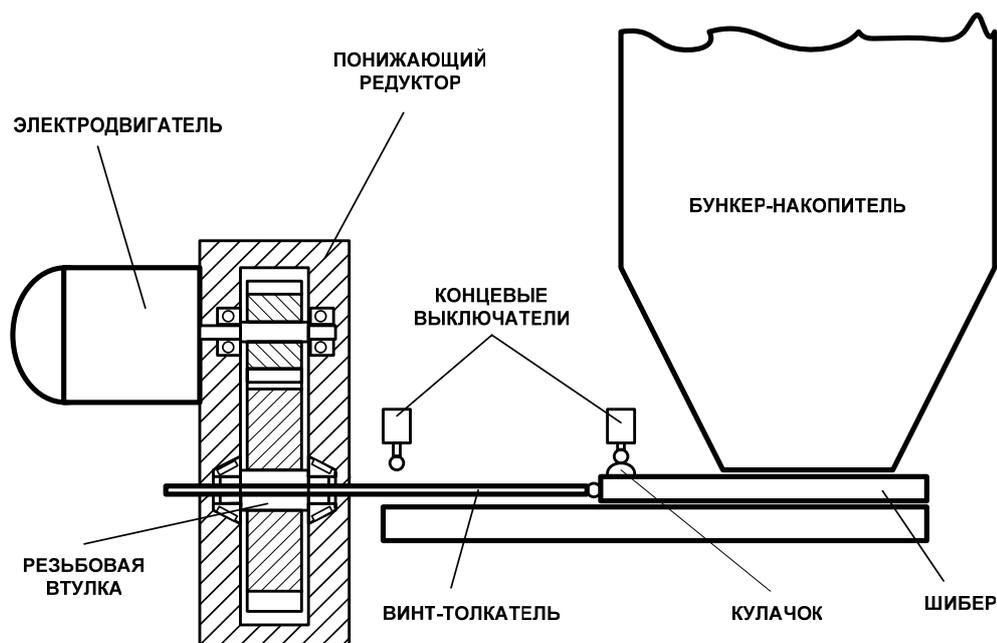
Исполнительный механизм шибера затвора бункера-накопителя
